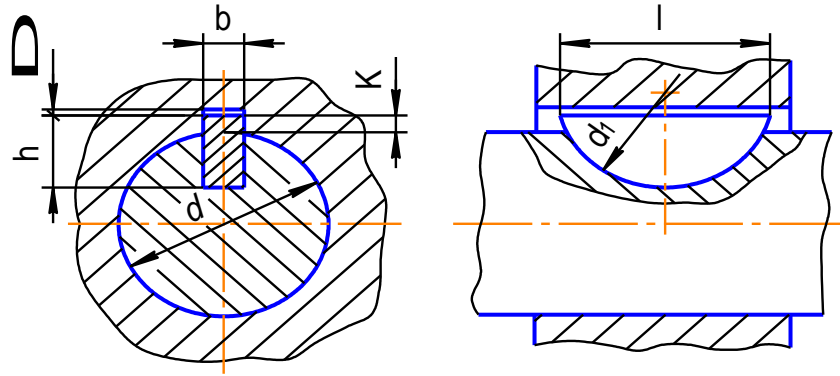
Конструкція шпонкового з'єднання сегментною шпонкою
